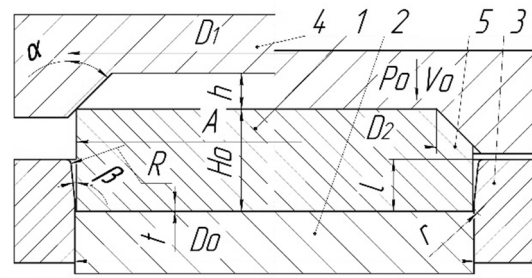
Схема гарячого осаджування фасок в кутових зонах заготовки квадратного перерізу: 1 – заготовка, 2 – плита, 3 – матриця, 4 – пуансон, 5 – zdeформована заготовка
